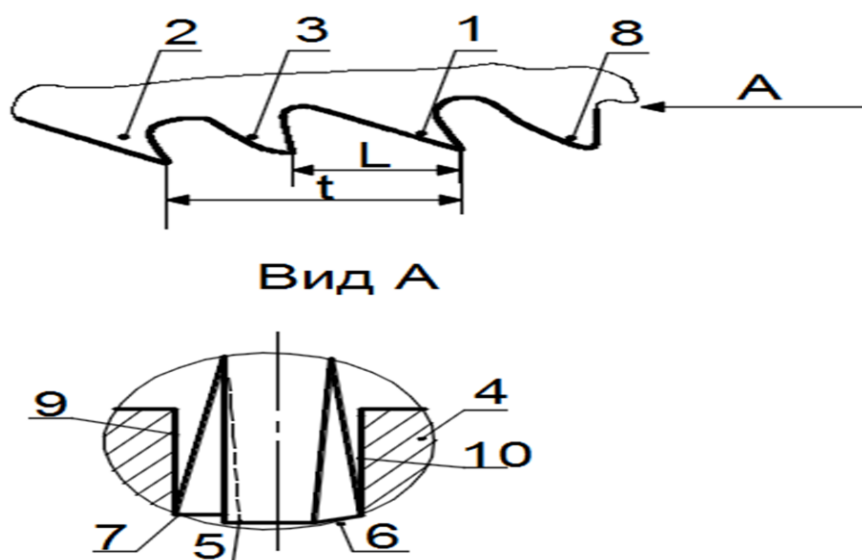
Схематичное представление типовой конструкции пилы [2]
